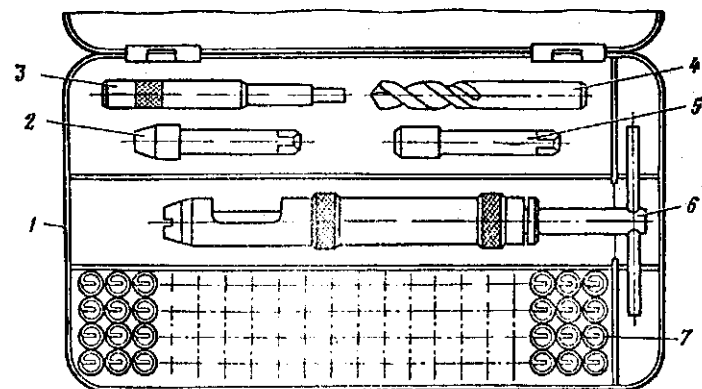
Комплект приспособлений для ремонта резьбовых отверстий спиральными вставками:
